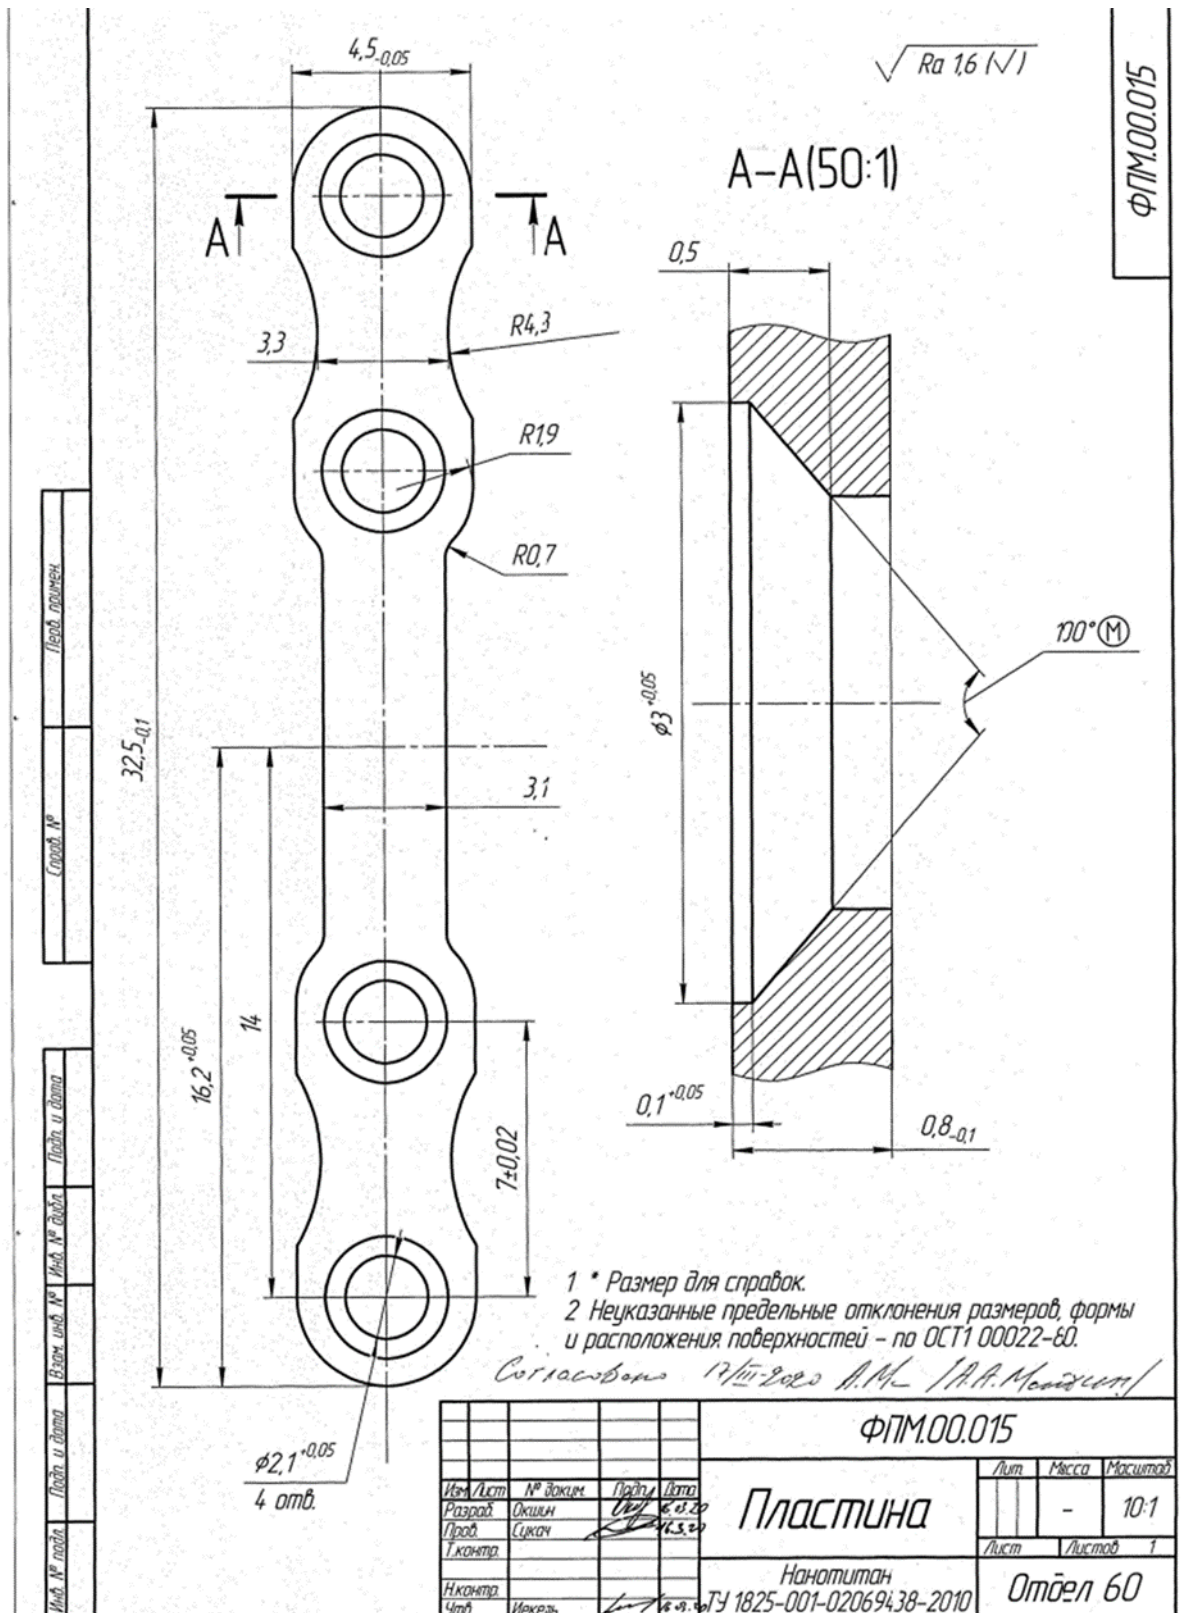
Конструкторский чертеж пластин из КЗ и из УМЗ титана
